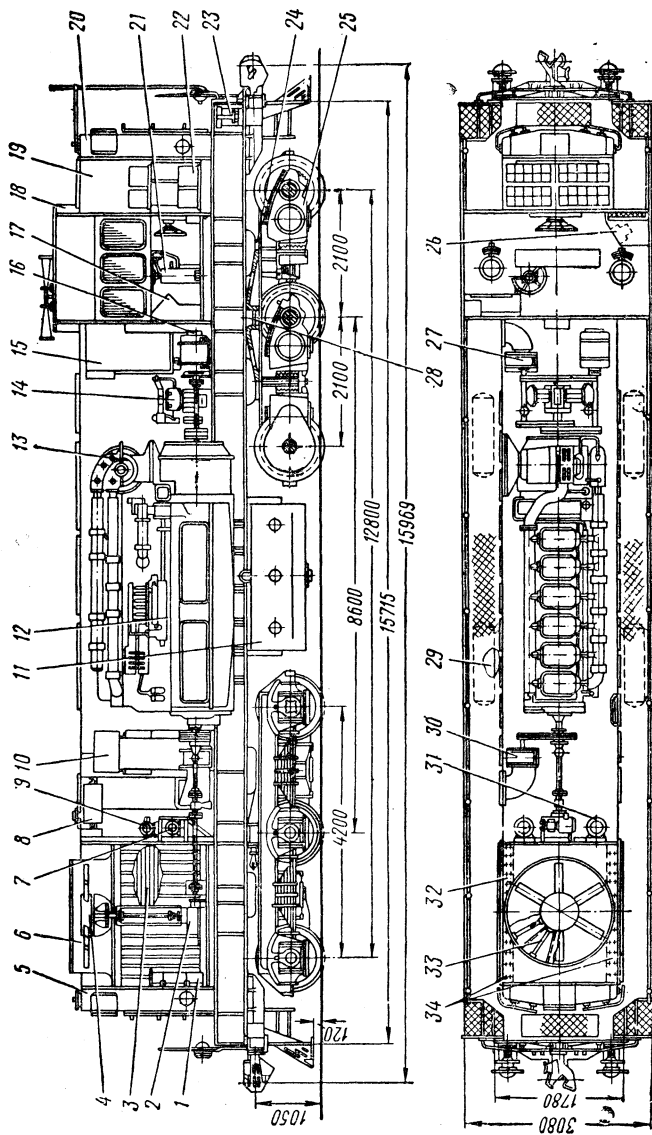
Продольный разрез и план тепловоза ТЭМ1:
